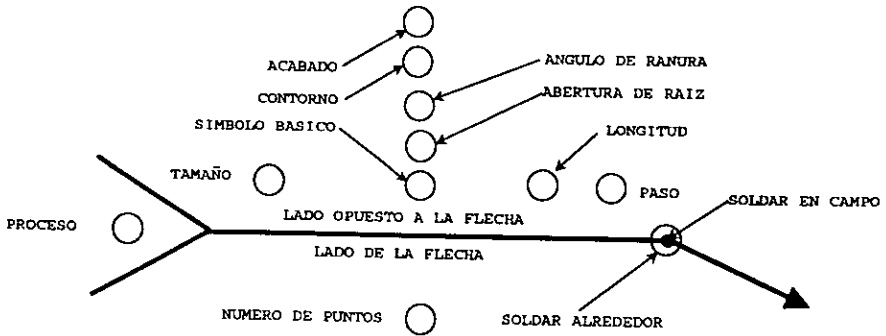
SIMBOLO DE SOLDADURA
